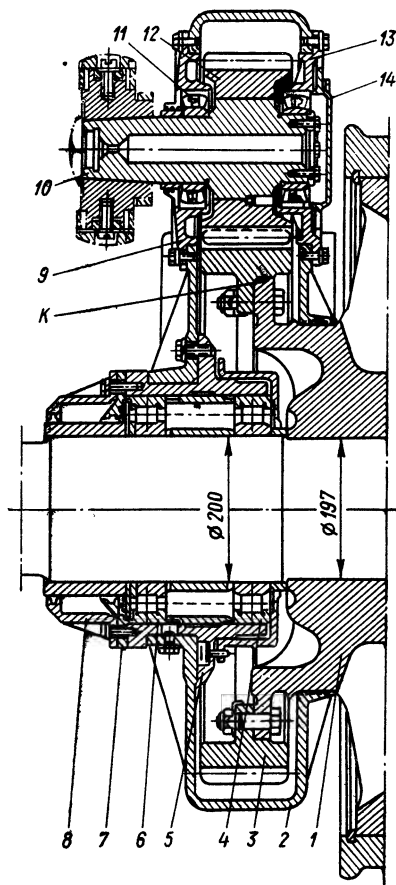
Зубчатый редуктор двигателя с карданной муфтой
